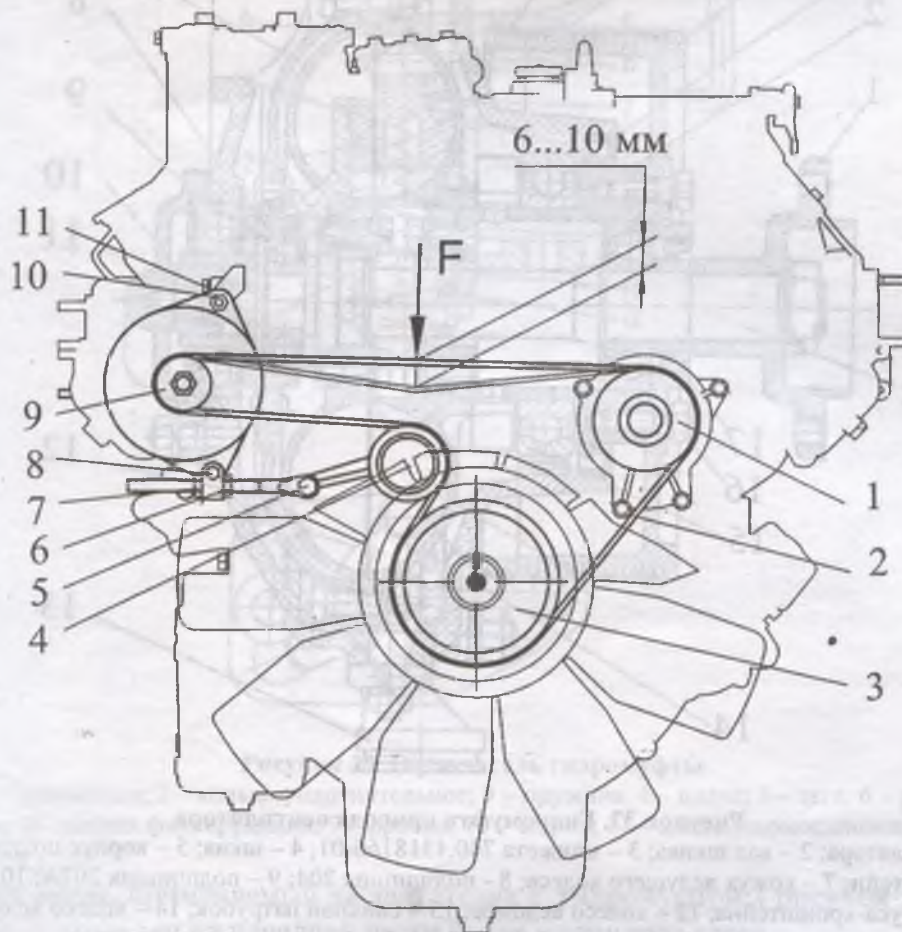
схема проверки натяжения ремней привода генератора и водяного насоса с расположением вентилятора по оси коленвала
